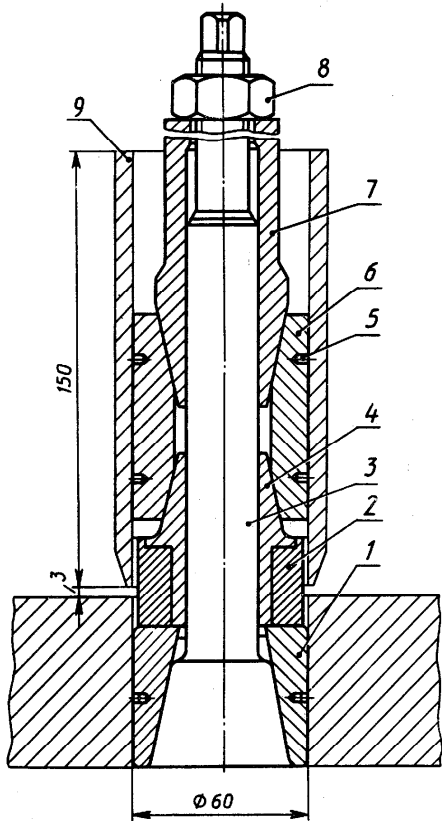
Приспособление для сборки и сварки штуцеров
